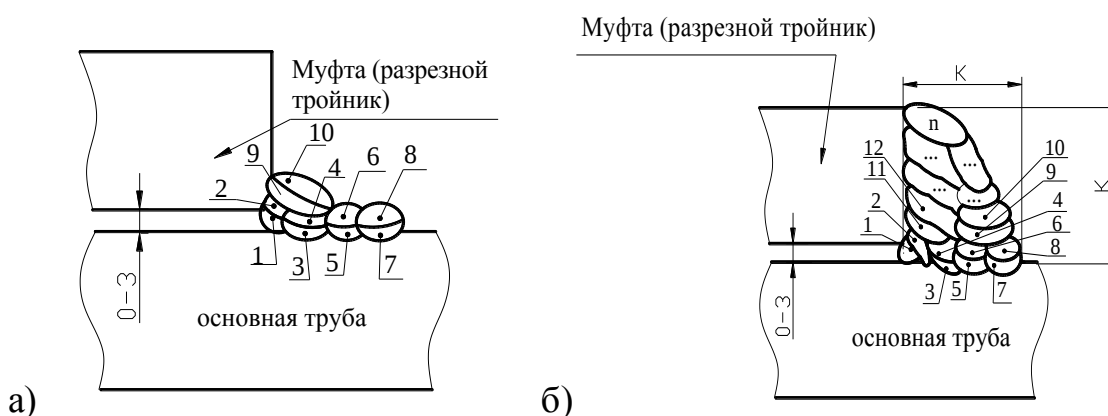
Последовательность при наложении слоев для сварки угловых швов без дополнительного подогрева
